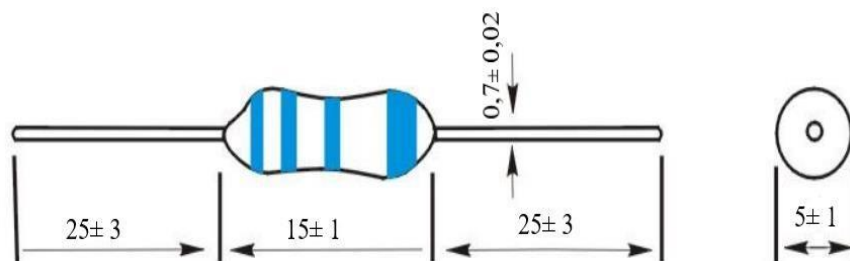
Габаритні розміри резистора KNP-200
